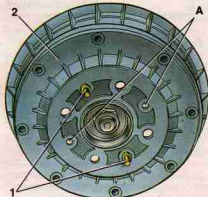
Тормозной барабан: 1 — направляющий штифт; 2 — тормозной барабан; А — резьбовое отверстие, используемое для снятия барабана
